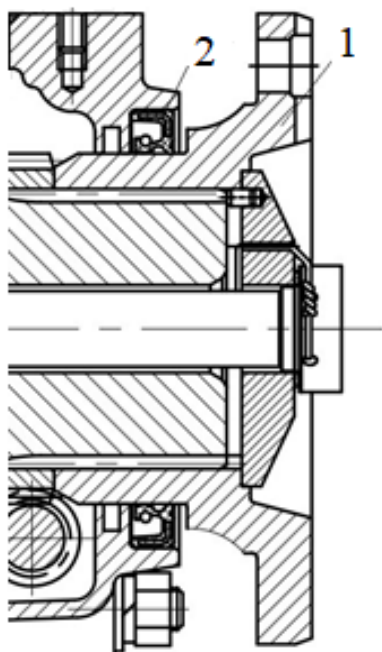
Эскиз соединения фланца с манжетой коробки передач ЯМЗ:
